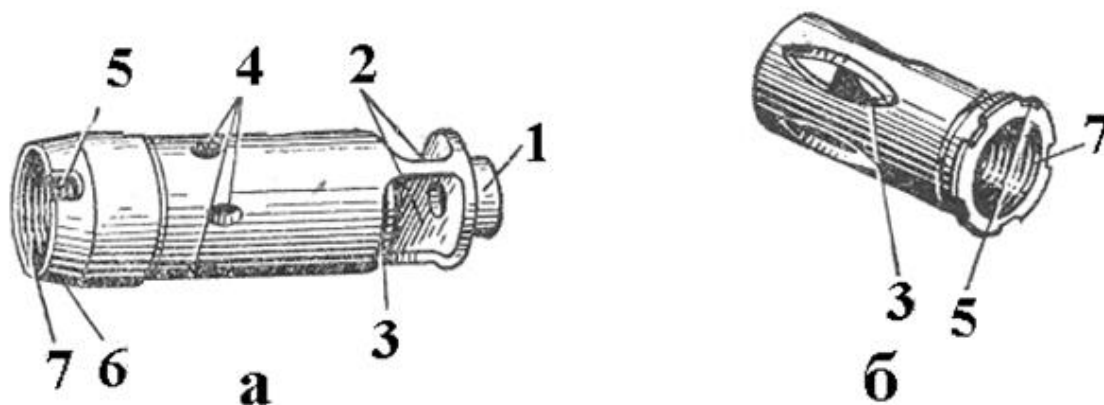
а, 33 б Дульный тормоз-компенсатор и пламегаситель
